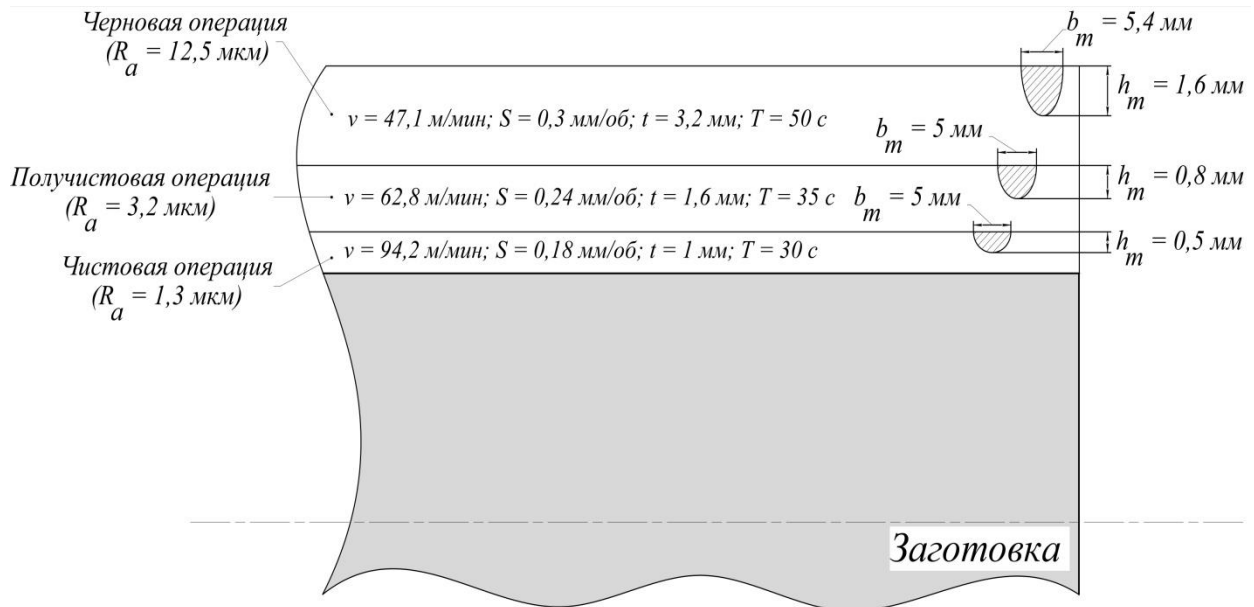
Схема расположения допусков и припусков с назначенными глубинами упрочненной мелкозернистой структуры (составлено автором)
